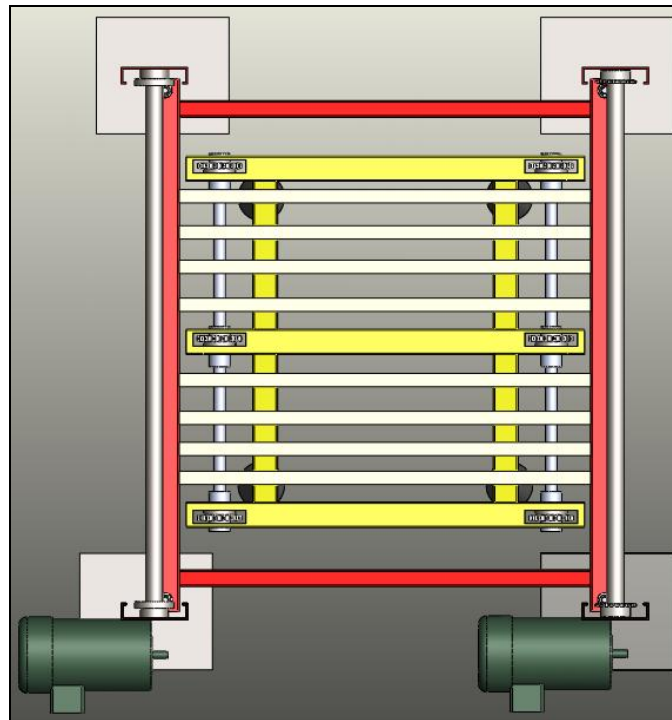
VISTA SUPERIOR SISTEMA DE ELEVACIÓN DE PALLET
